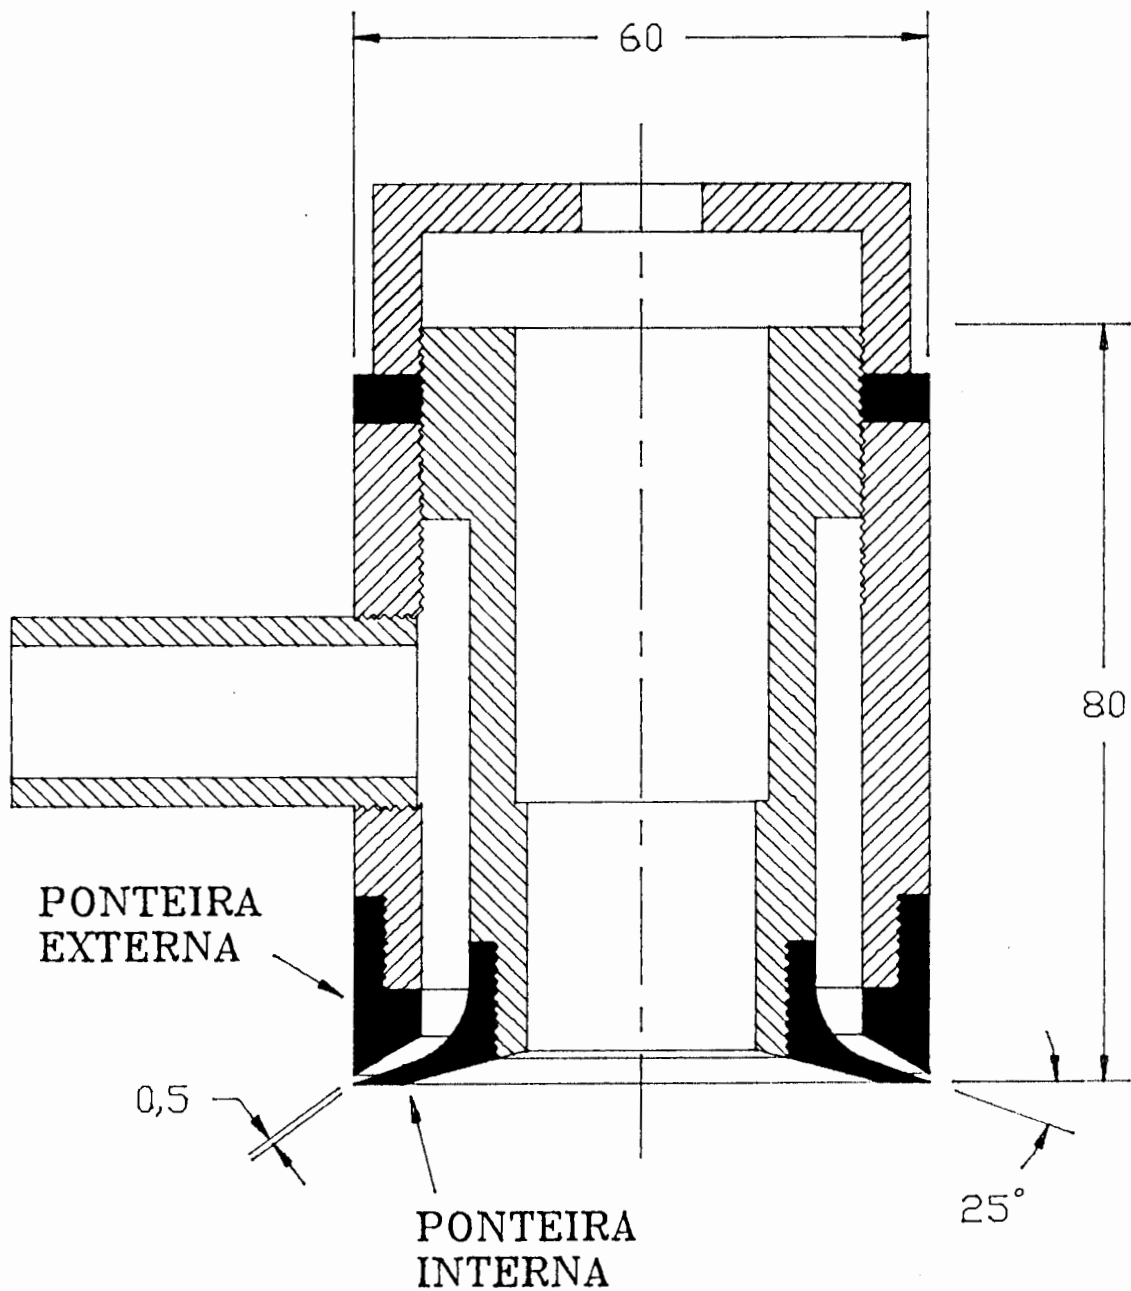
Desenho do bocal MIG/MAG de soldagem subaquática.
